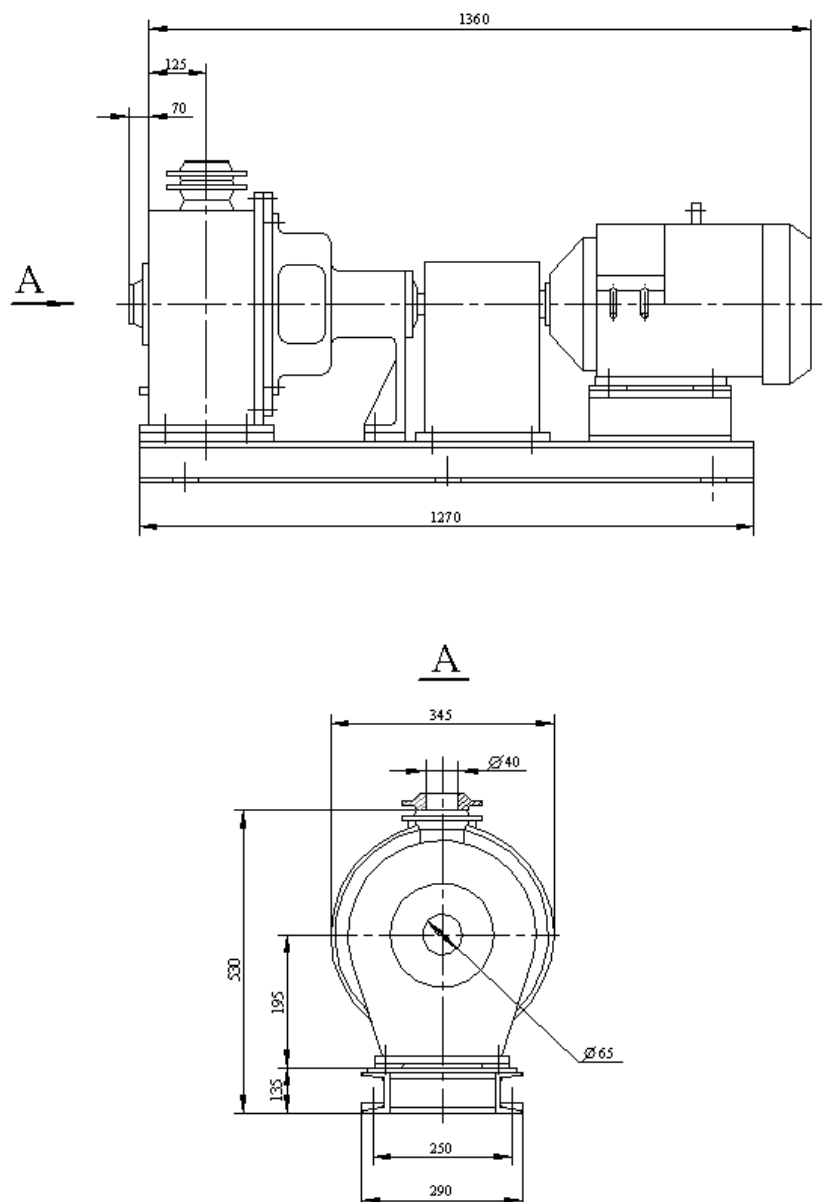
Габаритный чертеж насоса рециркуляции ванн ГЦН
